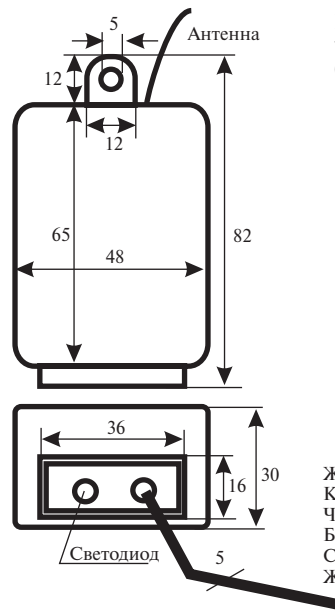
Габаритный чертеж основного блока СДУ MSRF-3D
